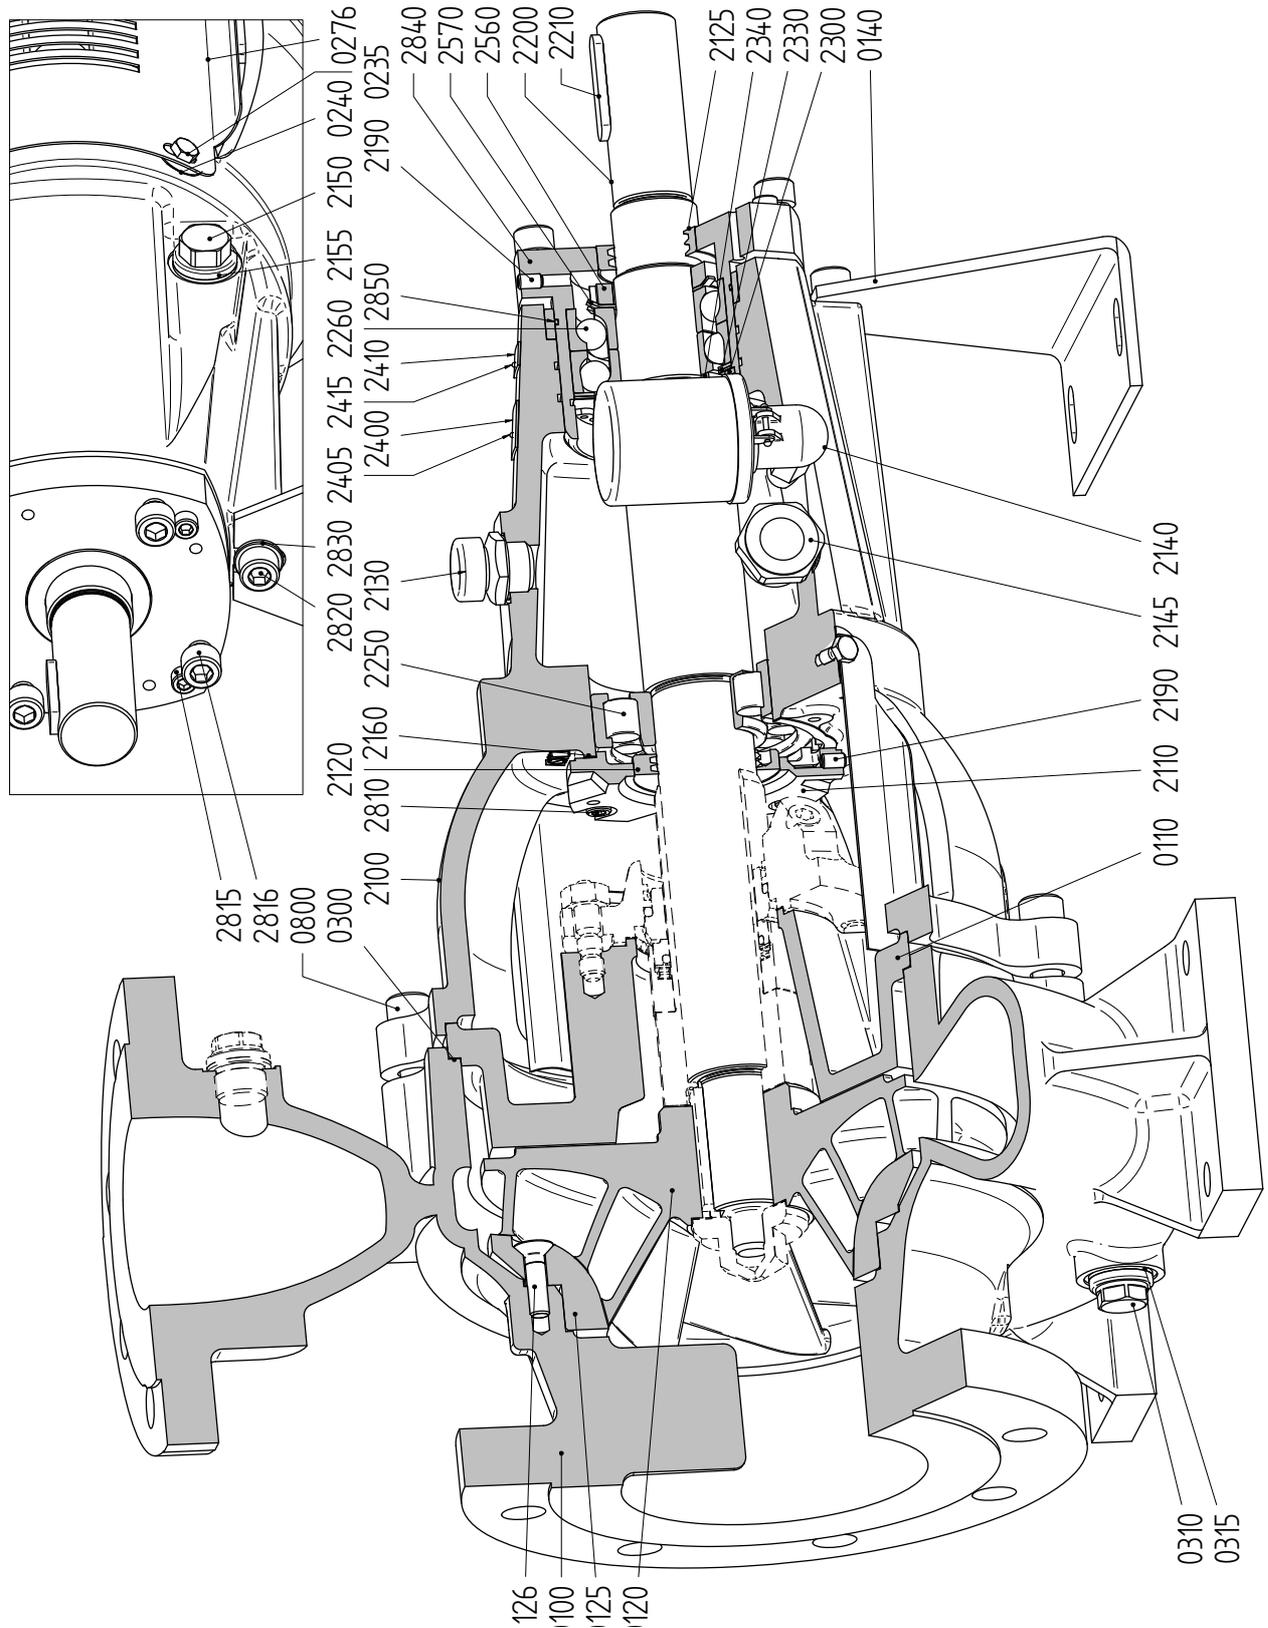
Schnittzeichnung L6 mit konischer Bohrung.
